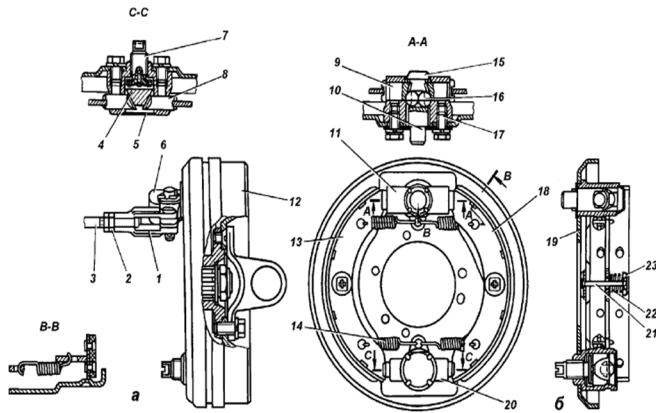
Стояночный тормоз барабанного типа:
